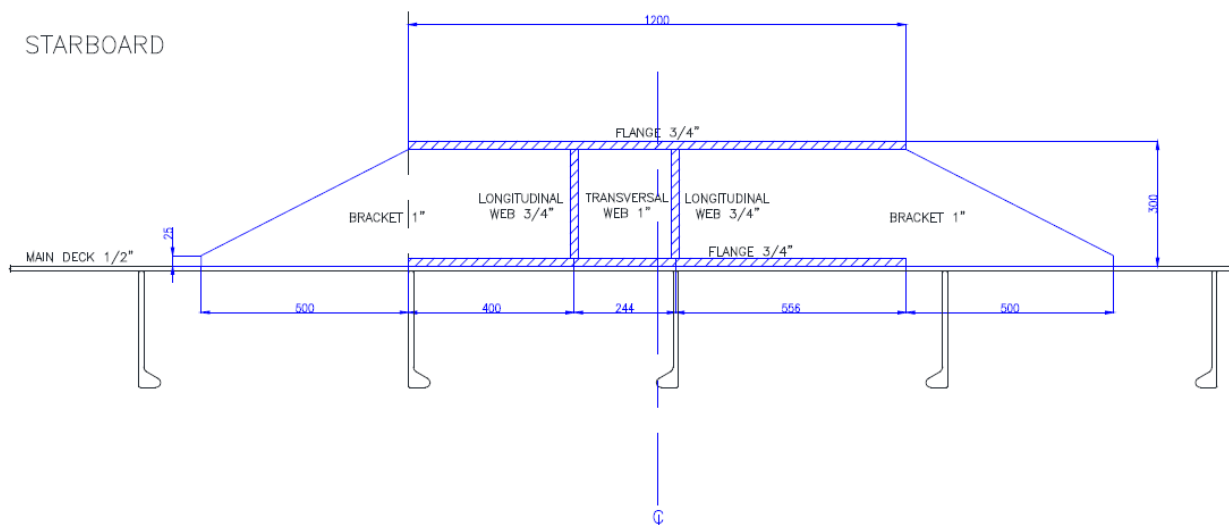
Vigas tipo NVA36 para refuerzo de cubierta principal de buque de apoyo a plataformas.
